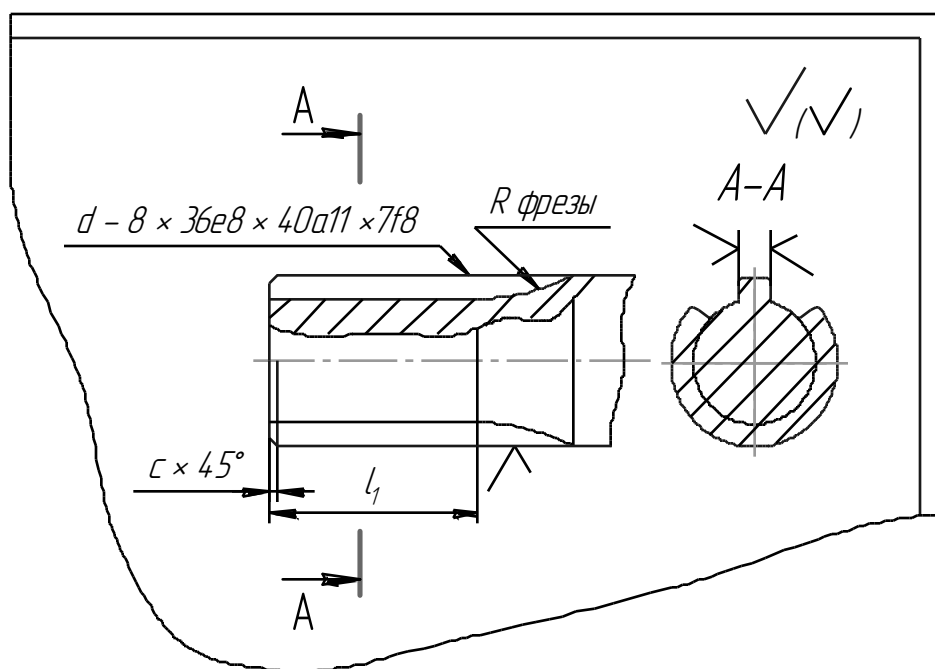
Чертеж шлицевого вала с прямобочным профилем зубьев
